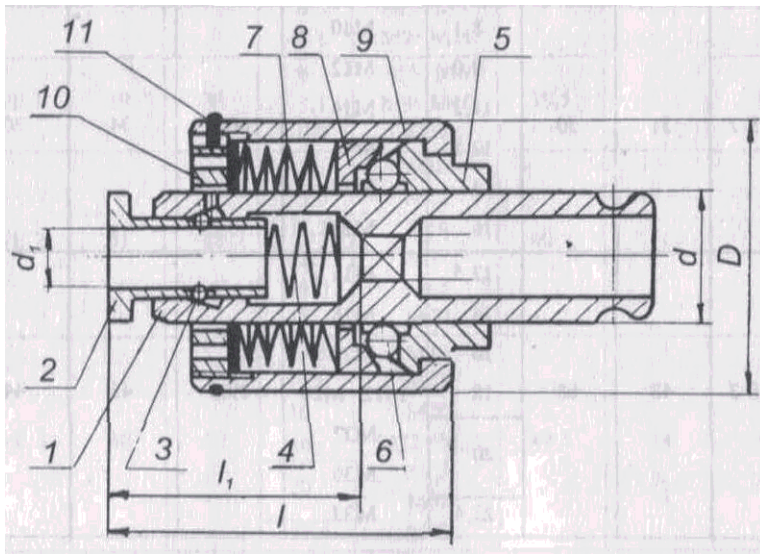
Быстросменная предохранительная головка для закрепления метчиков
